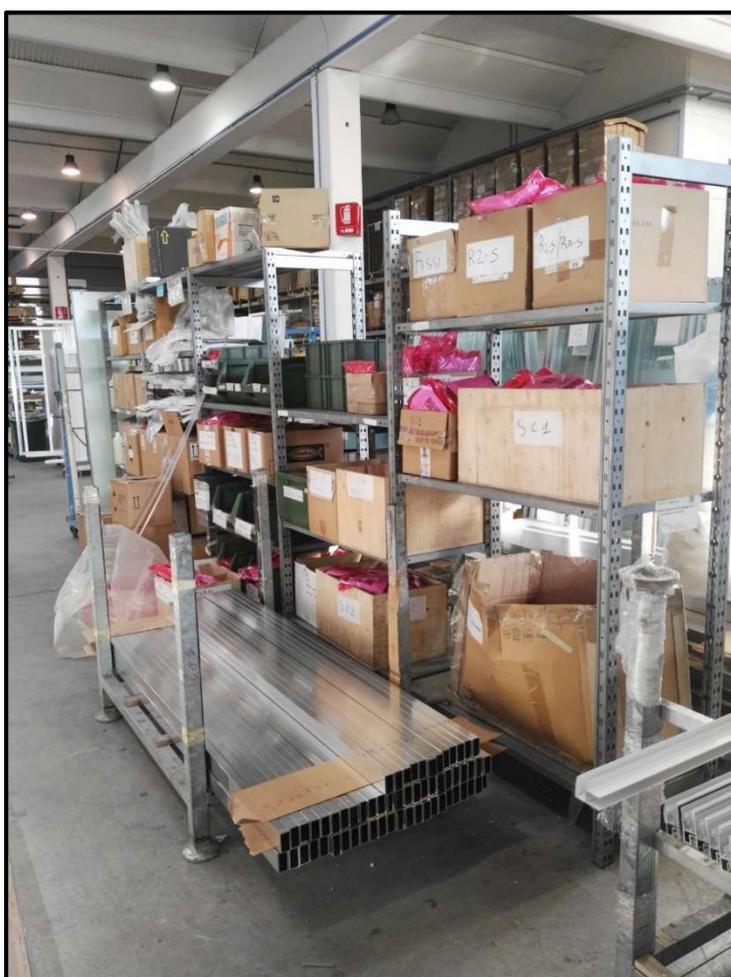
Buffer pezzi montati in attesa di essere imballati.
